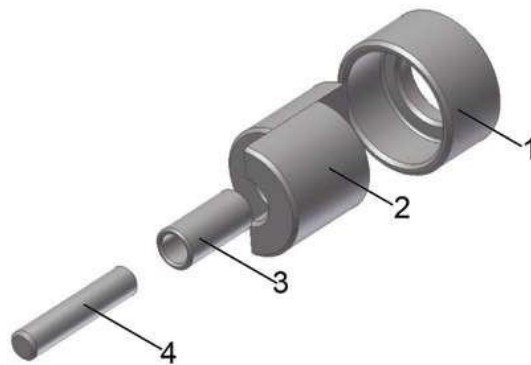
Приспособление для запрессовки диэлектрической опоры в кабельный соединитель ЖНКЮ.296361.014-01: 1 – основание, 2 – сегменты, 3 – втулка, 4 – стержень.
